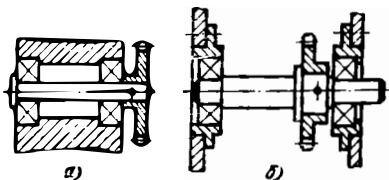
Варианты фиксации шаркоподшипников на валу и в корпусе
